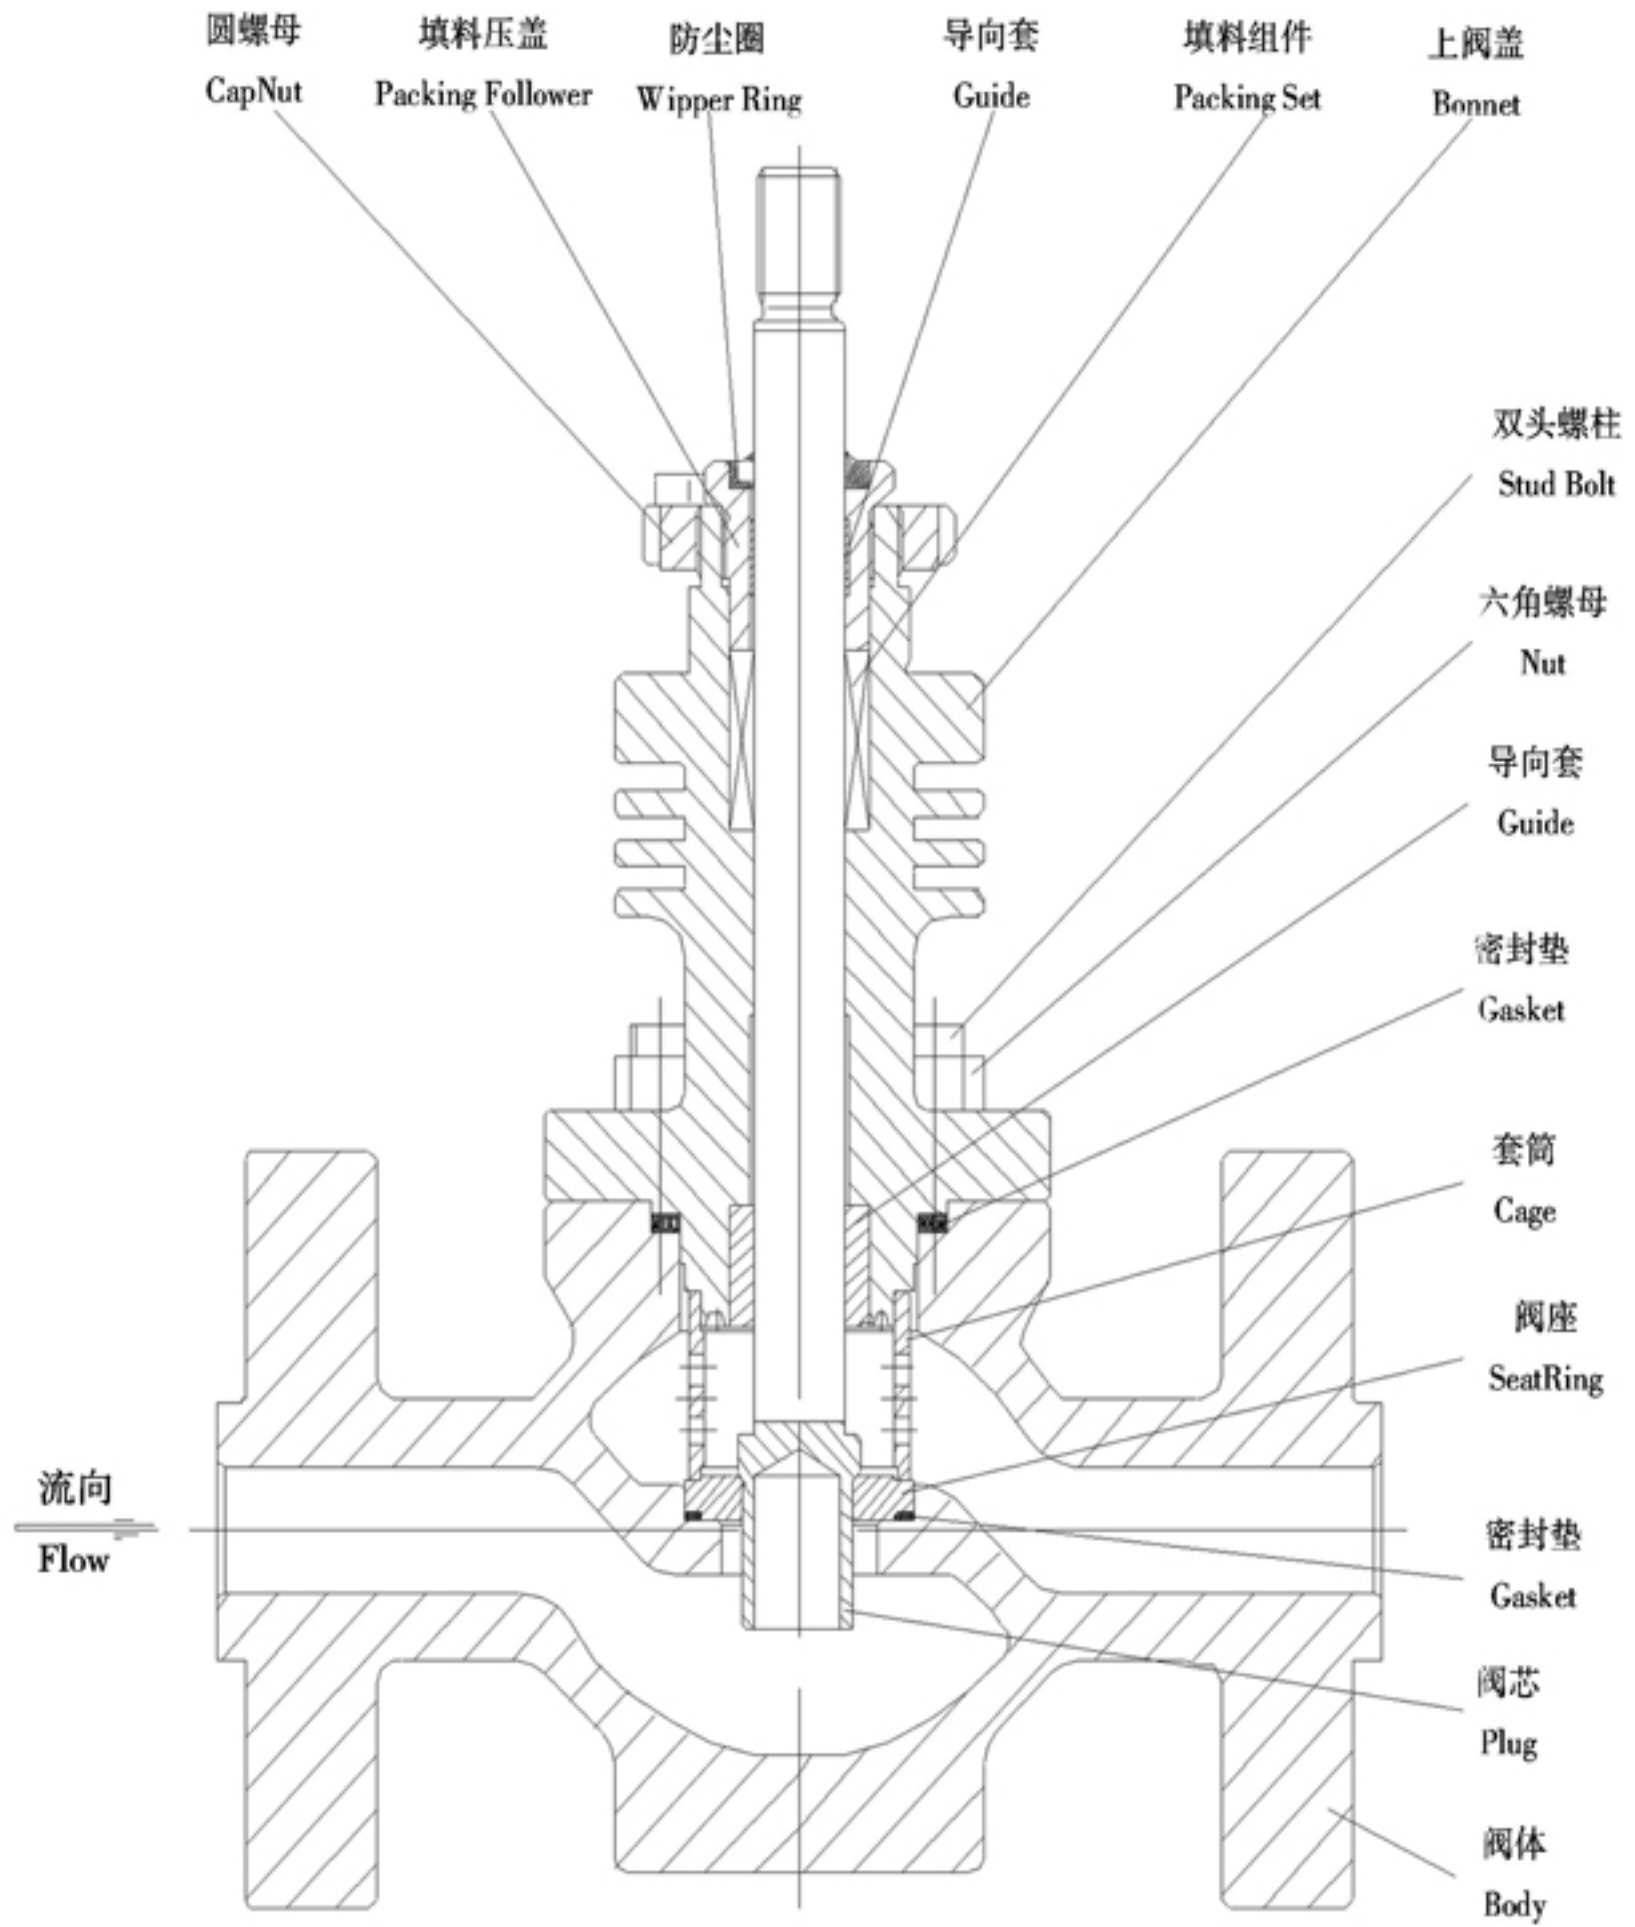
本体部构造 Fig.3 BODY SECTION VIEW
